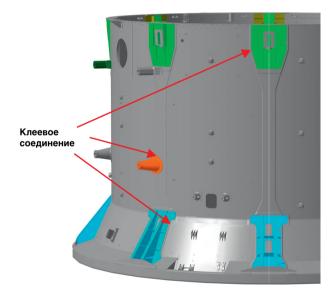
Элементы корпуса двигательного отсека, установленные с помощью клеевого соединения
